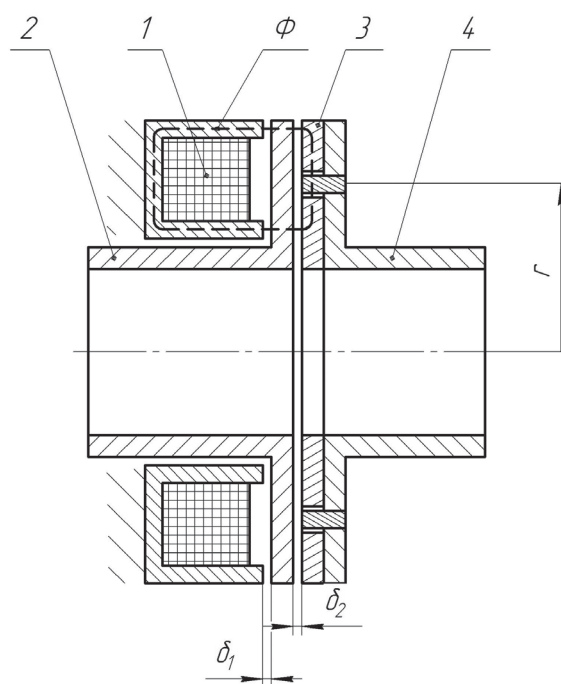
Конструктивная схема электромагнитной муфты сцепления: 1 — обмотка магнитопровода; 2 — ведущий вал; 3 — якорь; 4 — ведомый вал; Φ — магнитный поток; δ_1, δ_2 — воздушные зазоры
